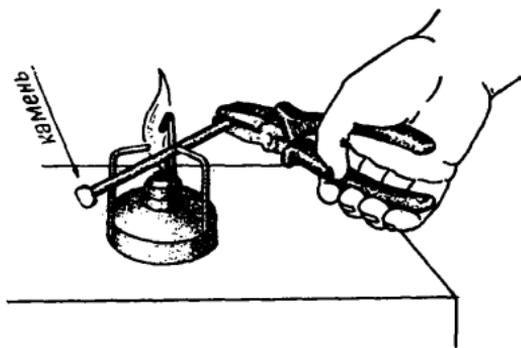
Съем обработанного камня с держателя путем его нагревания
